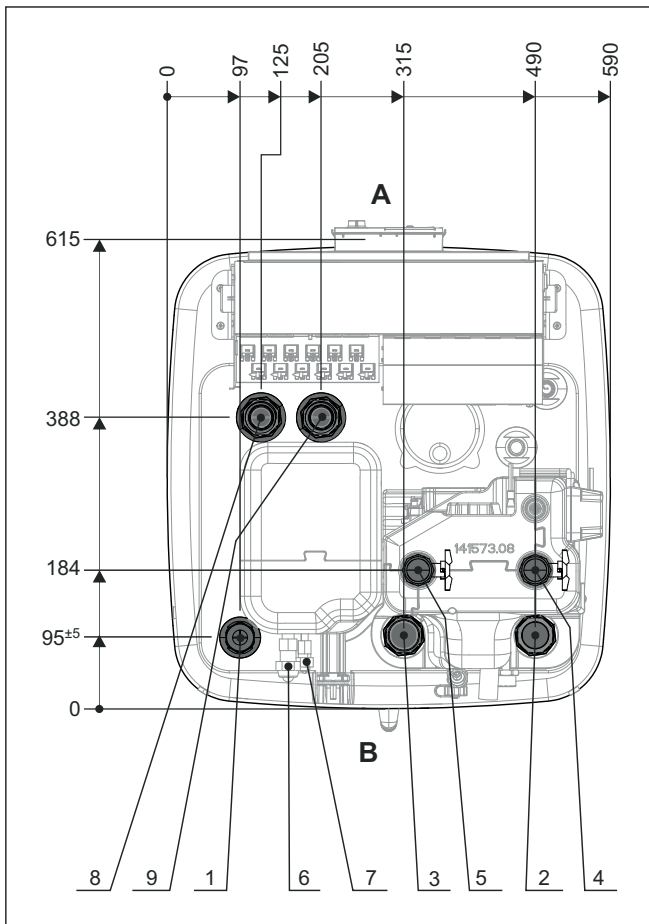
Dimensiones, lado superior del dispositivo - Tipo ... 04P30D/...08P30D
